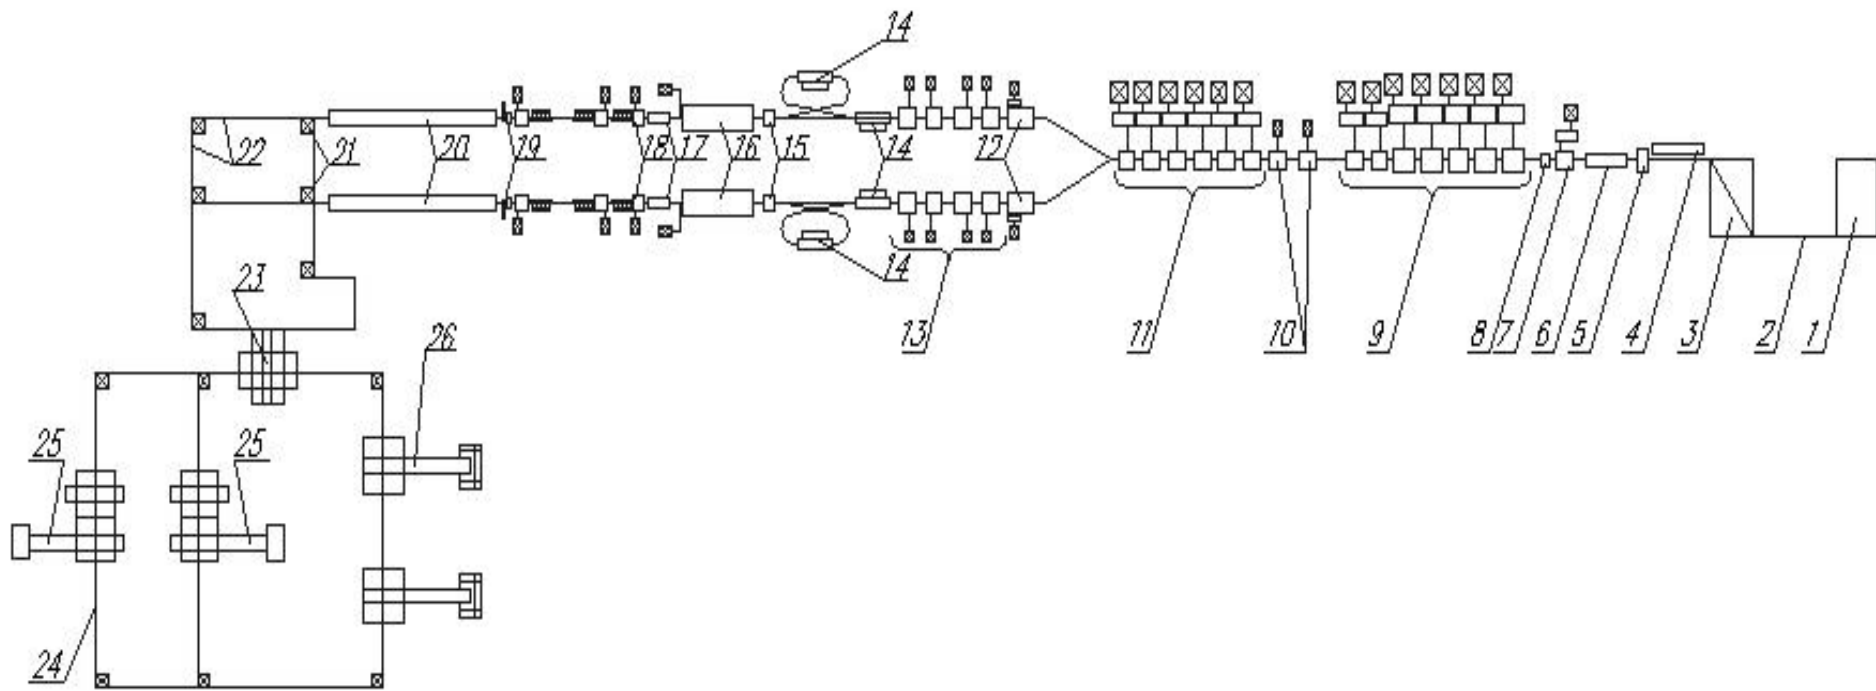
Схема расположения оборудования мелкосортно-проволочного стана 150: 1-загрузочная решетка; 2-рольганг загрузочный; 3-печь нагревательная; 4-стол для отбраковки заготовок; 5-гидросбив окалины; 6-термостат; 7-трайбаппарат; 8-ножницы; 9-черновая группа клеток; 10-ножницы обрезные; 11-промежуточная группа клеток; 12-ножницы обрезные; 13-предчистовая группа клеток (4×2); 14- линия водяного охлаждения; 15-ножницы обрезные; 16-чистовой проволочный блок; 17-линия водяного охлаждения проката; 18- трайбаппарат; 19-виткоукладчик; 20-линия воздушного охлаждения проката; 21-виткосборник; 22-линия транспортировки бунтов; 23- передаточная тележка бунтов; 24-крюковой конвейер бунтов; 25-установка подпрессовки и обвязки бунтов; 26-разгрузочная тележка бунтов.
